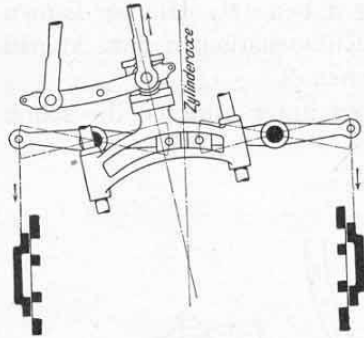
Steuerung zur oszillierenden Maschine der Fig. 566.
